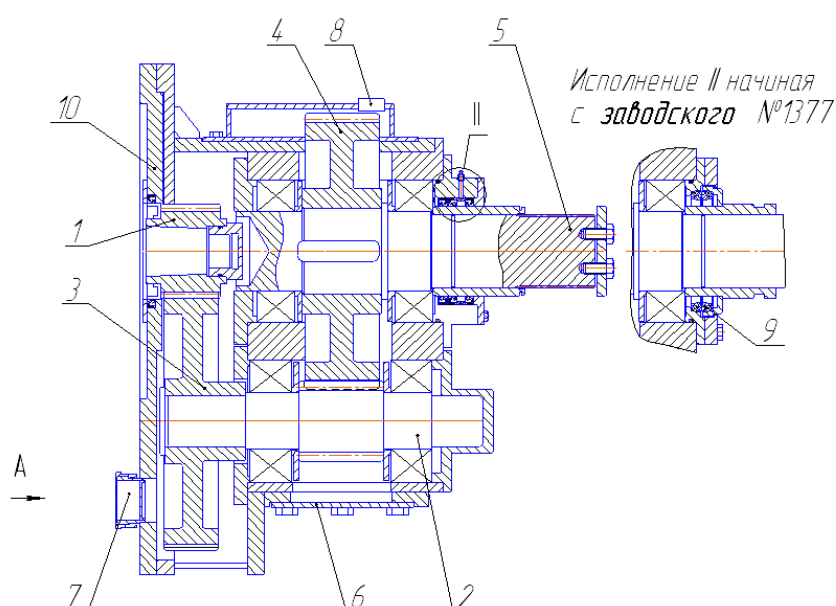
Редуктор: 1 - ведущая шестерня; 2 - вал-шестерня; 3 - колесо; 4 - колесо; 5 - вал; 6 - крышка; 7 - сапун; 8 - сливная заглушка; 9 – уплотнение торцевое TLDOA 1830; 10 – фланец
